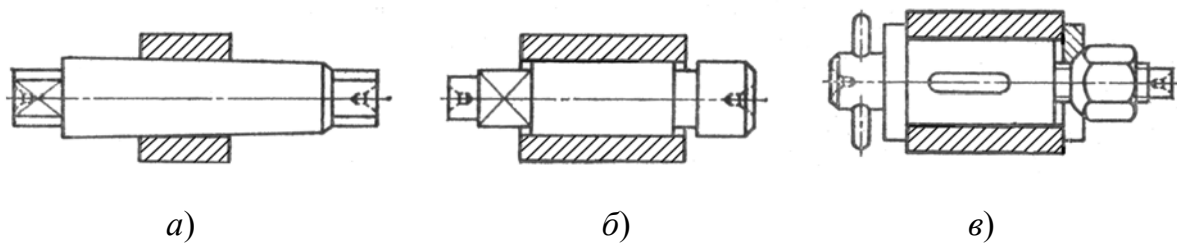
Жесткие оправки: а – коническая; б – цилиндрическая для установки с натягом; в – цилиндрическая для установки с зазором
